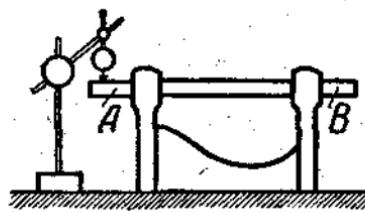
Проверка индикатором параллельности оси шинделя и направляющих станины винторезно-токарного станка.
